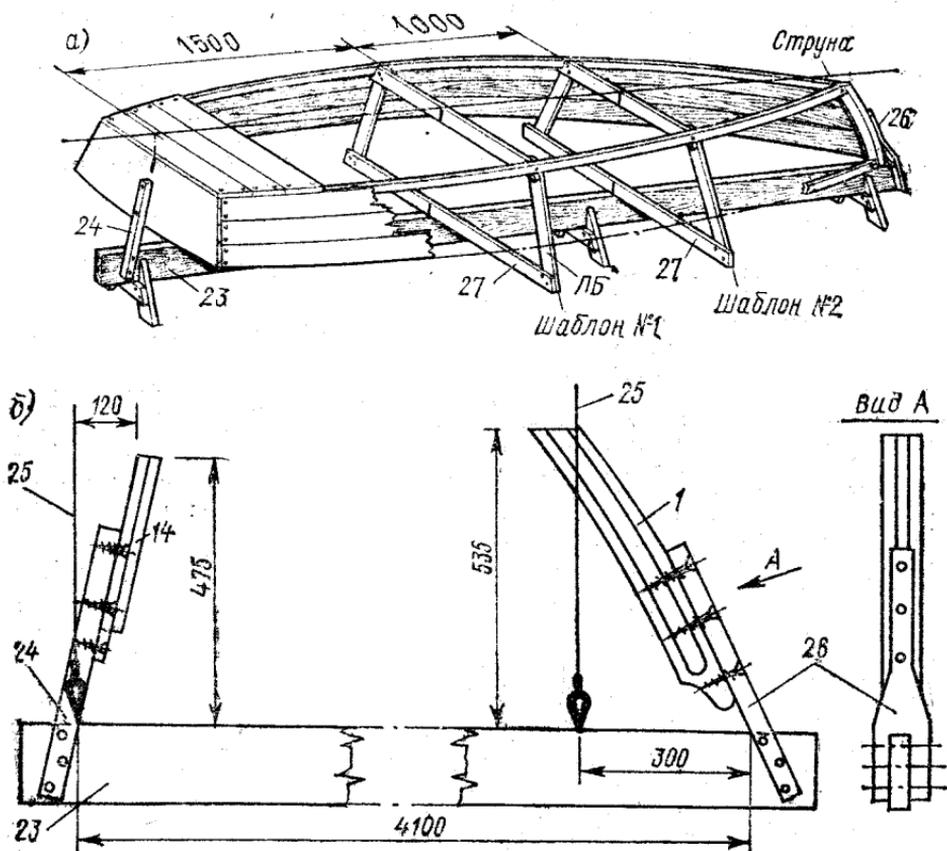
Схема сборки корпуса на стапеле (а); проверка установки форштевня и транца (б).
